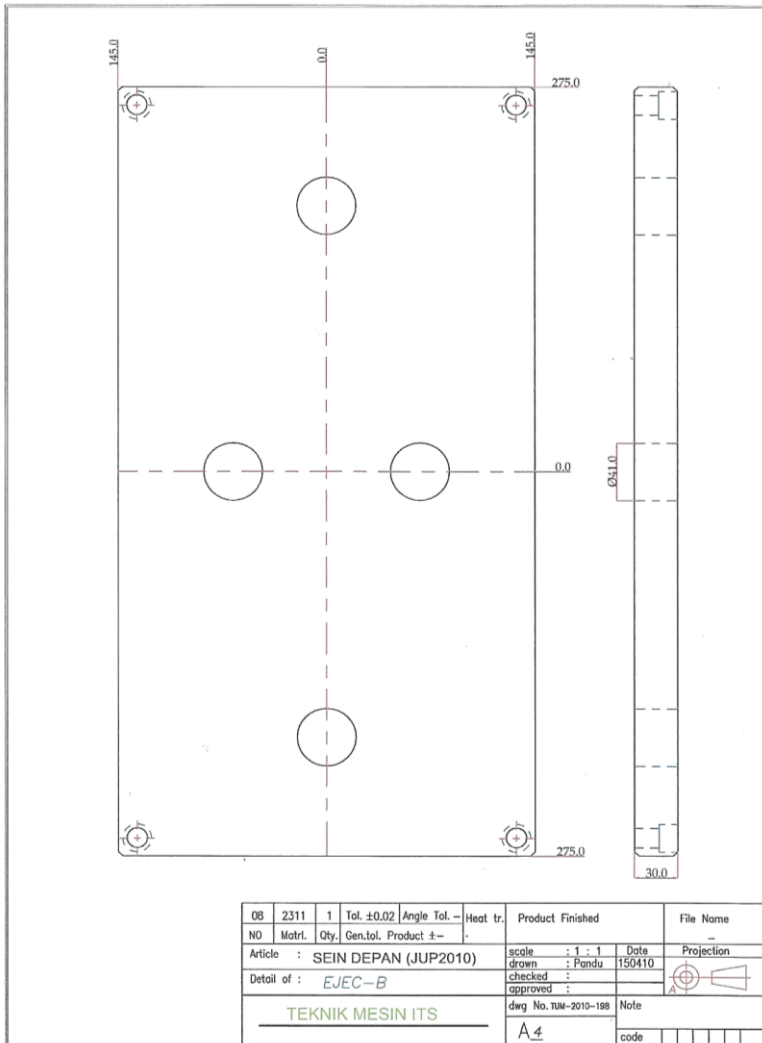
Detail drawing 2D untuk komponen *bottom plate
